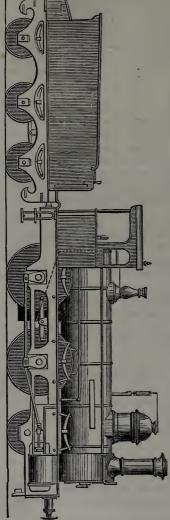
Machine à six roues, construite par Borsig (de Berlin).
